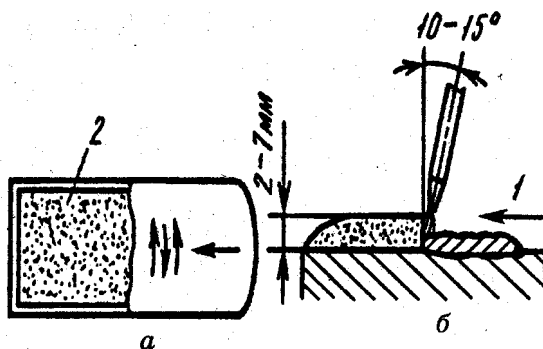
Положение угольного электрода в процессе наплавки порошкообразных твердых сплавов:
